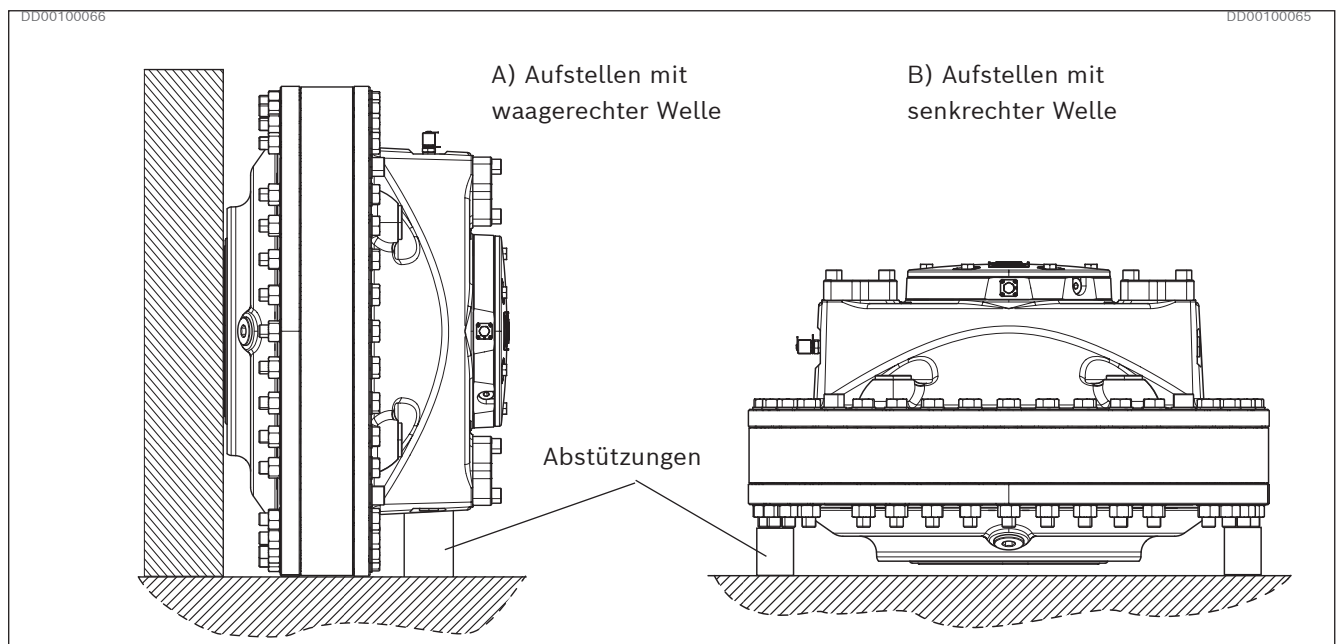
Aufstellen des CB-Motors auf einer flachen Oberfläche (Beispiel)
